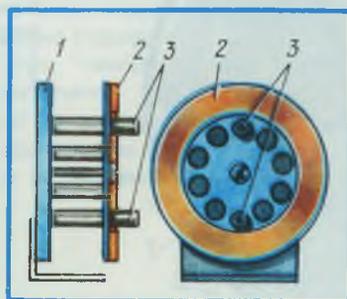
Крепление кольца к катушке: 1 — катушка; 2 — кольцо; 3 — ручки.
